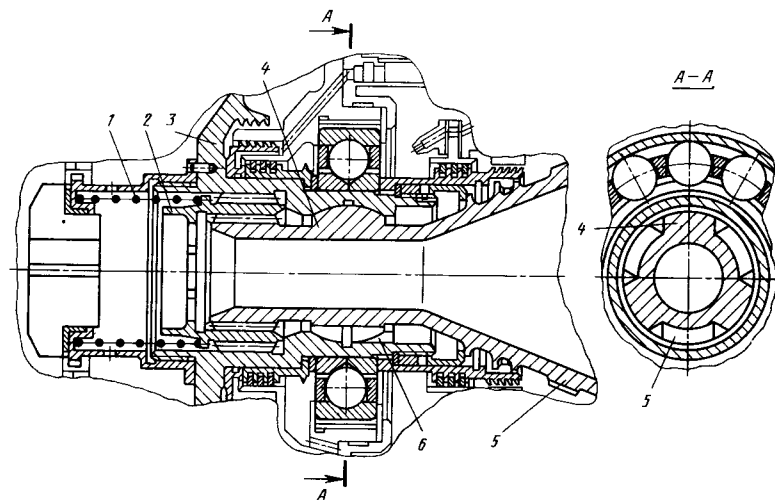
Соединение роторов осевого компрессора и газовой турбины ТВД ТВ2-117
